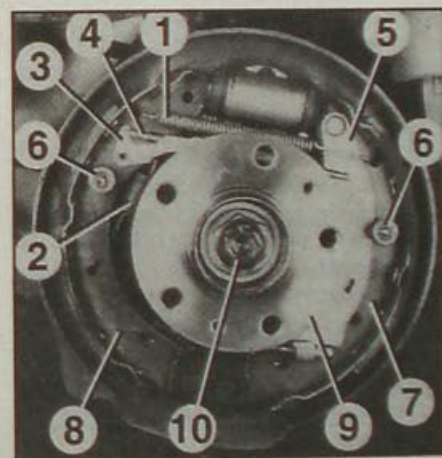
Элементы заднего барабанного тормозного механизма:
